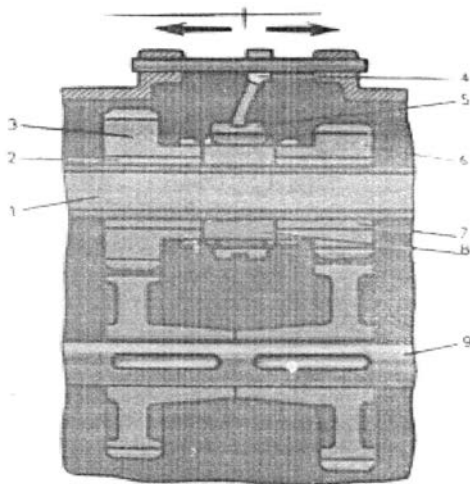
Коробка передач: 1-ведущая шестерня 2-й передачи; 2-скалка; 3-рычаг; 4-вилка; 5- ведущая шестерня 1-й передачи; 6-первичный вал; 7-шестерны заднего хода; 8-ведущая шестерня 1-й передачи и заднего хода; 9-вал заднего хода; 10-ведомая шестерня заднего хода; 11-вторичный вал; 12-ведомая шестерня 2-й передачи; 13- главная передача; 14-фиксатор.
